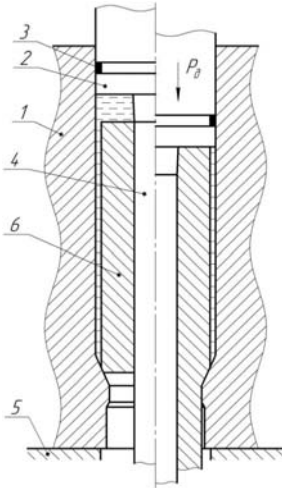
Схема гидропрессования трубчатых заготовок на оправке
